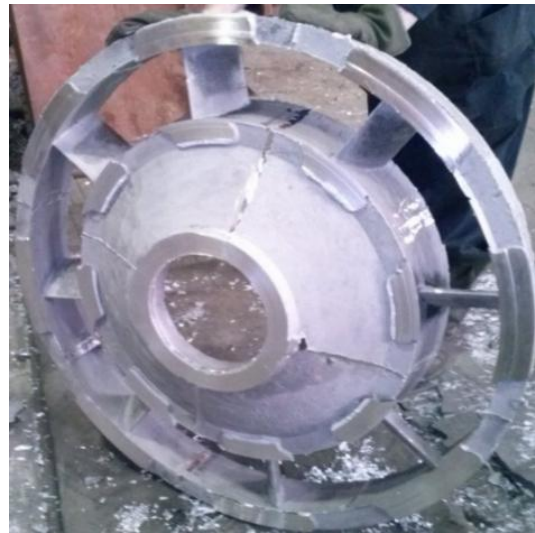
Корпусные детали двигателя НК-32, изготовленные из серийных жаропрочных литейных магниевых сплавов МЛ9, МЛ10, МЛ19
